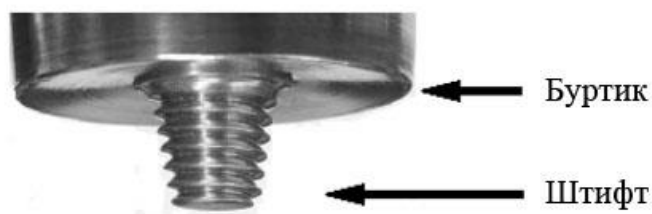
Конструкция инструмента для сварки трением с перемешиванием
